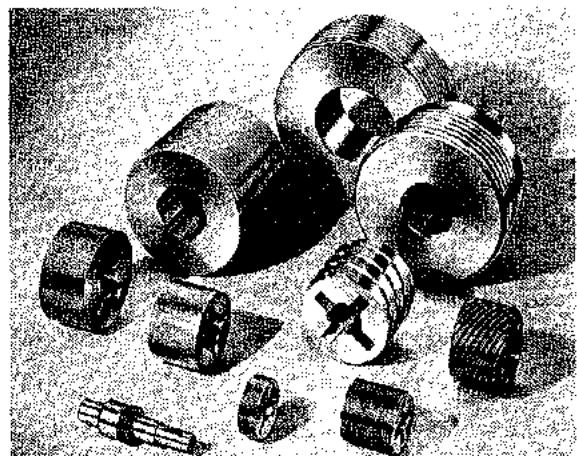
Matrices cilíndricas para el laminado de roscas (Reed Rolled Thread Die Co.)
